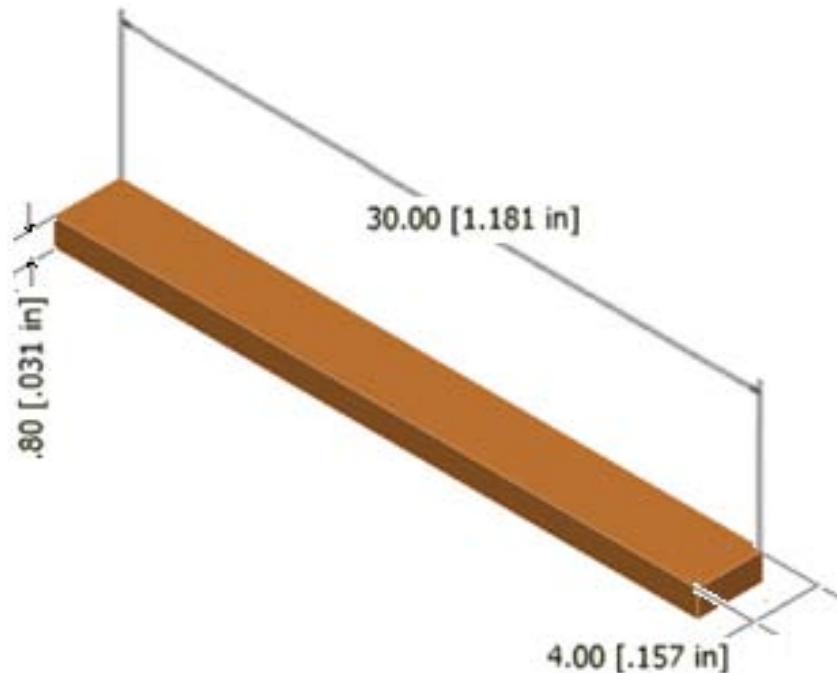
Arreglo de una viga en cantiléver sujeta a flexión.
